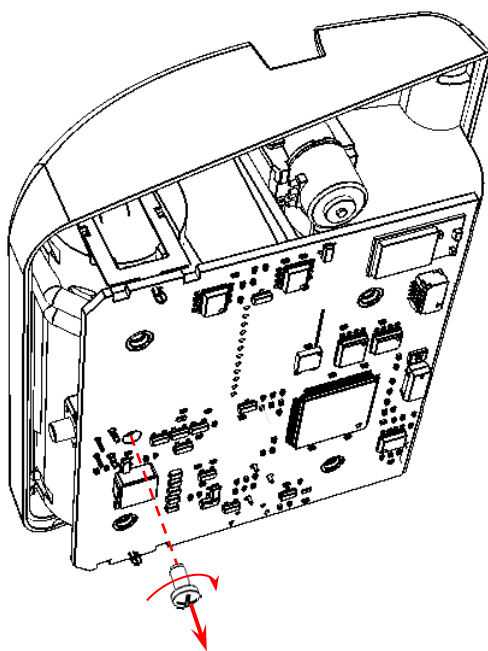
Винт крепления БУ к верхней части корпуса ККТ
